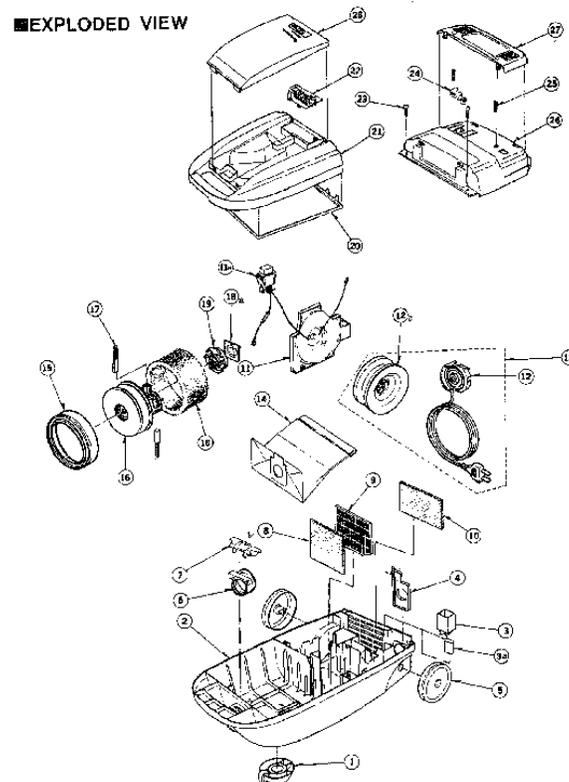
Aspirateur standard vue éclatée (Searspartsdirect.com, s.d.)
